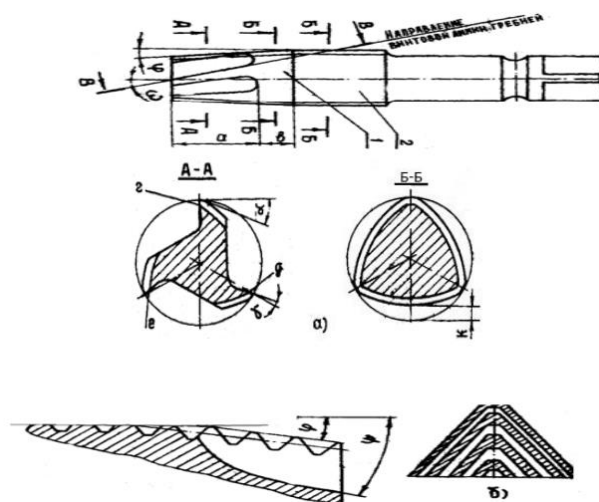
Режуще-выдавливающий метчик: а) конструкция режуще-выдавливающего метчика; б) схема образования резьбы метчиком
